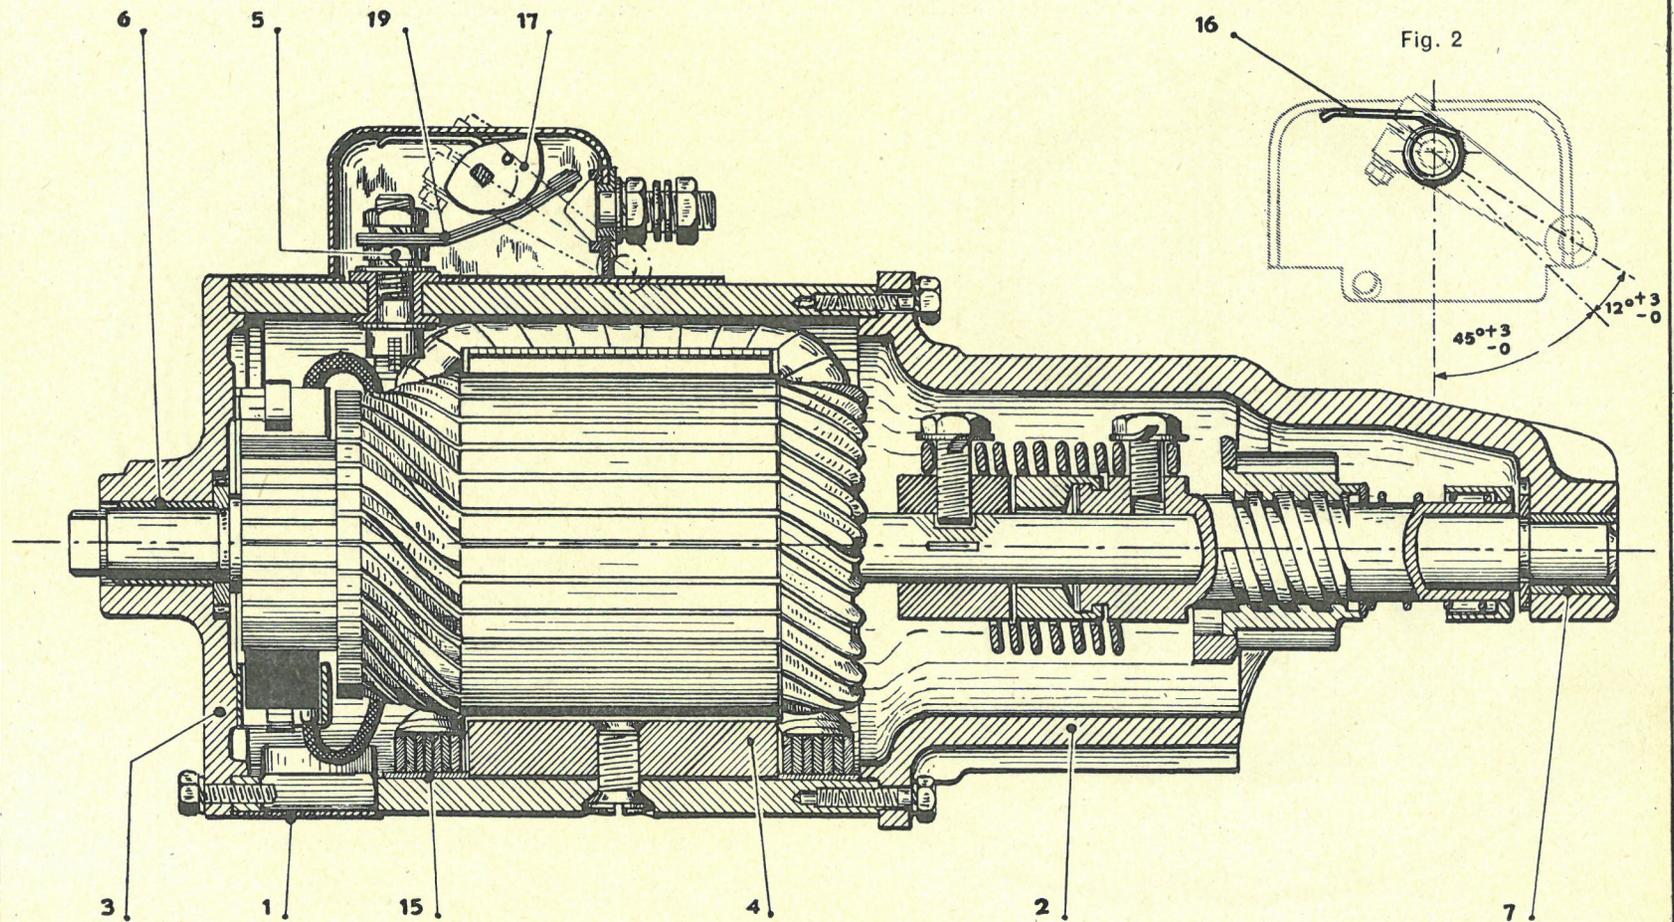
ENSEMBLE DES BOBINES INDUCTRICES
